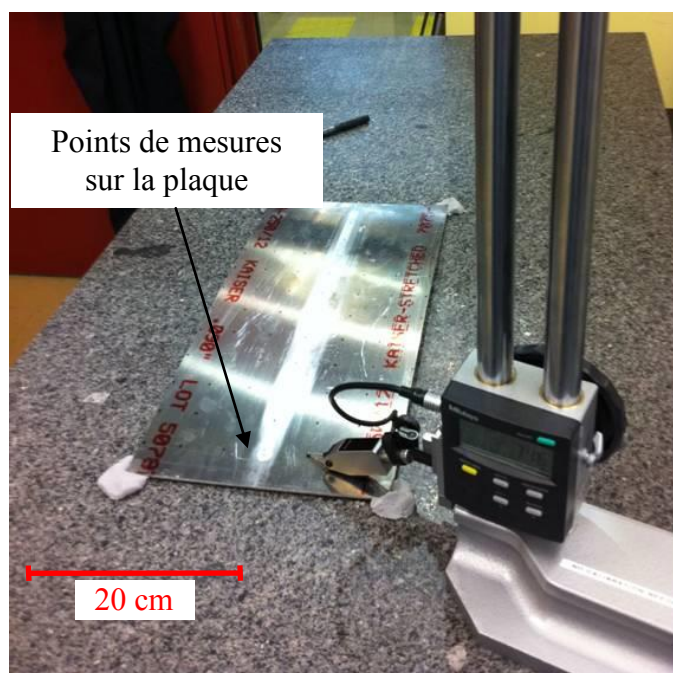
Mesures des défauts de planéité des plaques soudées.
